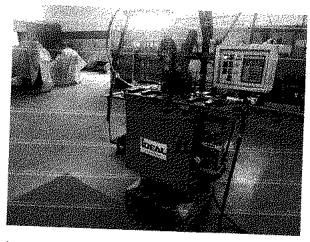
Maquina de Solda para Serra de Fita marca Ideal Schweißmaschinen referencia BAS 120S
